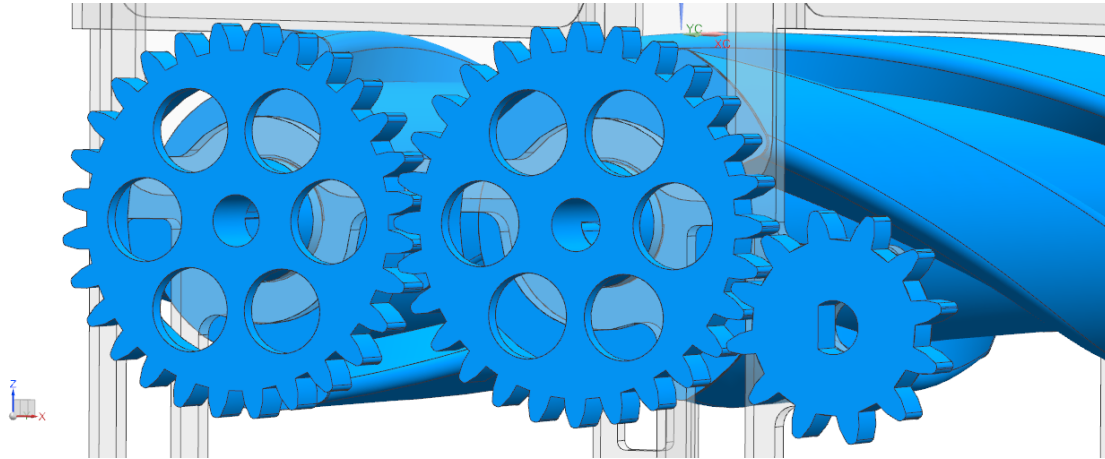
Vista detalle del mecanismo de transmisión mediante engranajes / Fuente: Propia
